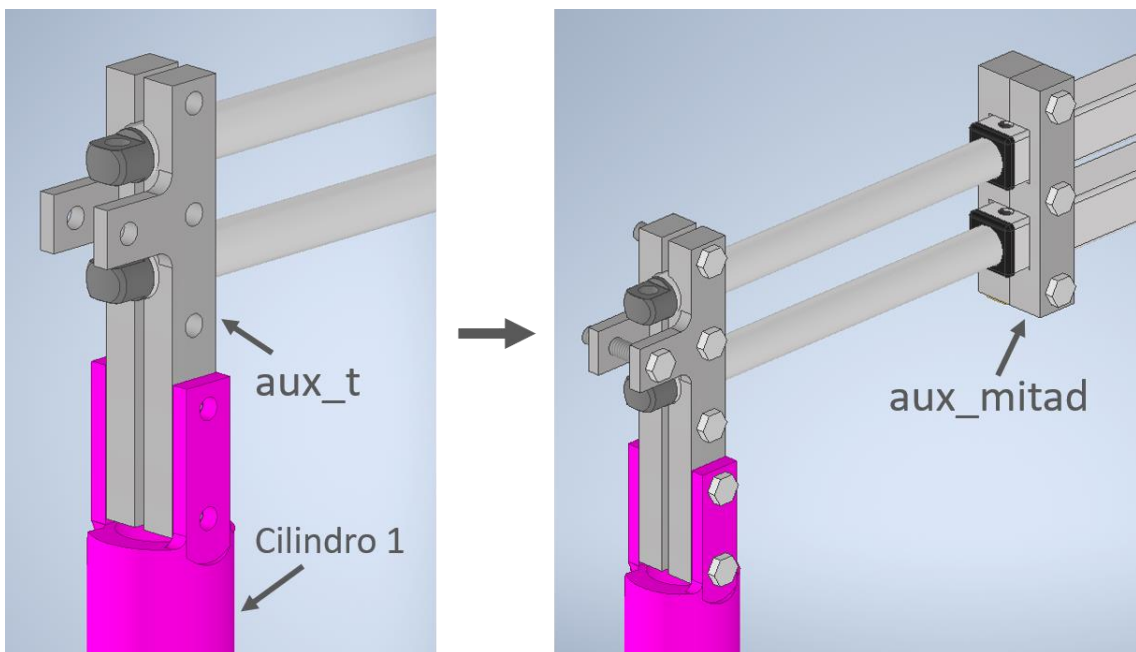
Montaje de las piezas aux_t y aux_mitad
